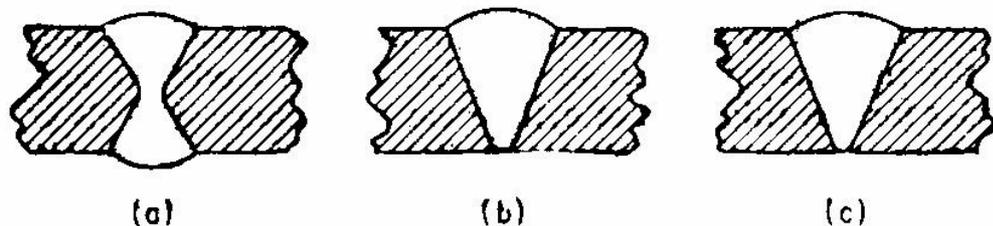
Tipos de soldadura: *a)* Junta por ensamble de soldadura doble, picada antes de soldar el segundo lado. *b)* Junta por ensamble de soldadura simple, con banda de respaldo que puede o no retirarse. *c)* Junta por ensamble de soldadura simple, sin banda de respaldo (que sólo se permite para algunas soldaduras perimetrales).
